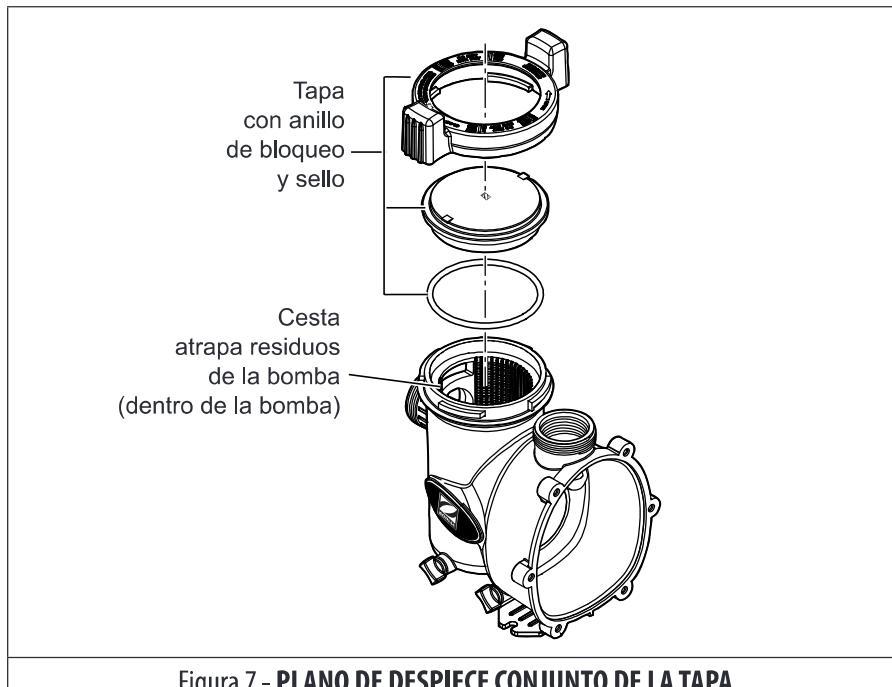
PLANO DE DESPIECE CONJUNTO DE LA TAPA
